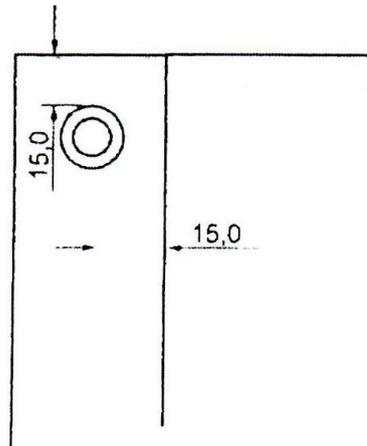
Tralha com ilhós - Fonte: ABNT NBR 162867:2014
